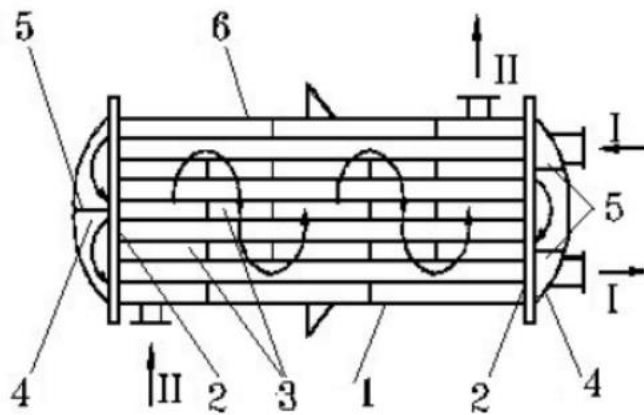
Багатоходовий кожухотрубчастий теплообмінник:
